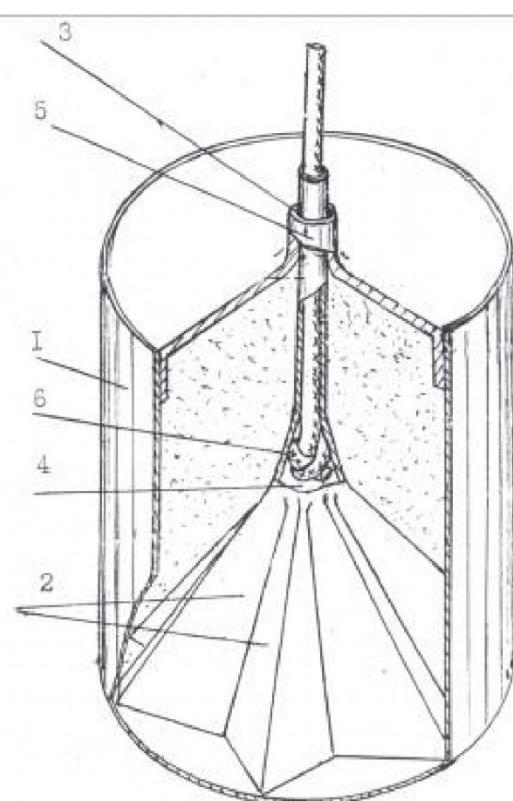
Профилированный кумулятивный заряд ПКЗ-0,4с с узлом крепления ДШ в виде осевой полости: 1 - оболочка; 2 - V-образные кумулятивные элементы; 3 - трубчатый элемент с осевой полостью; 4 - коническое углубление; 5 - крышка с цилиндрическим отверстием; 6 - ДШ
